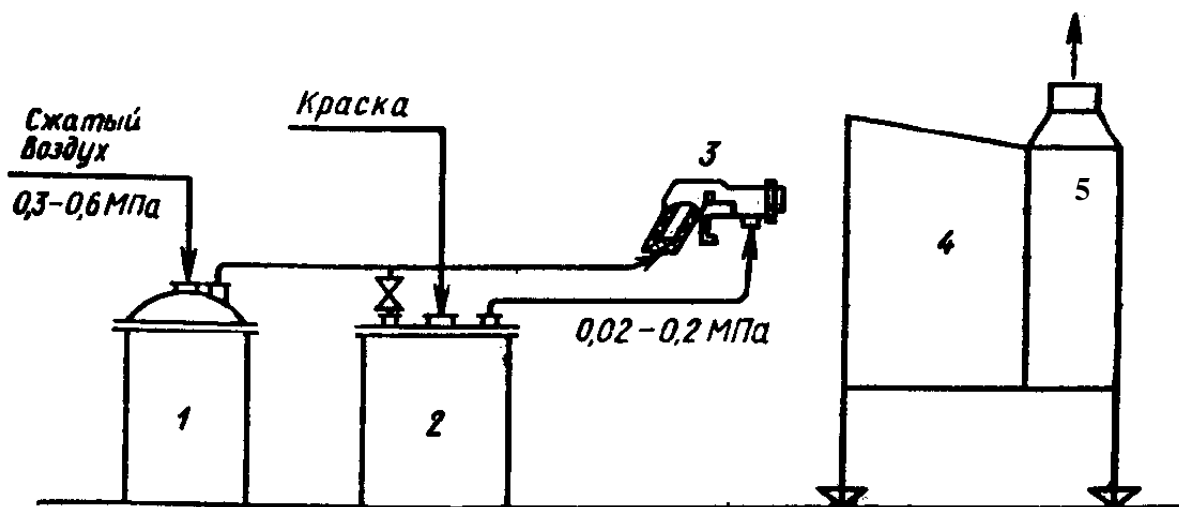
Схема установки для ручного нанесения ЛКМ пневматическим распылением:
